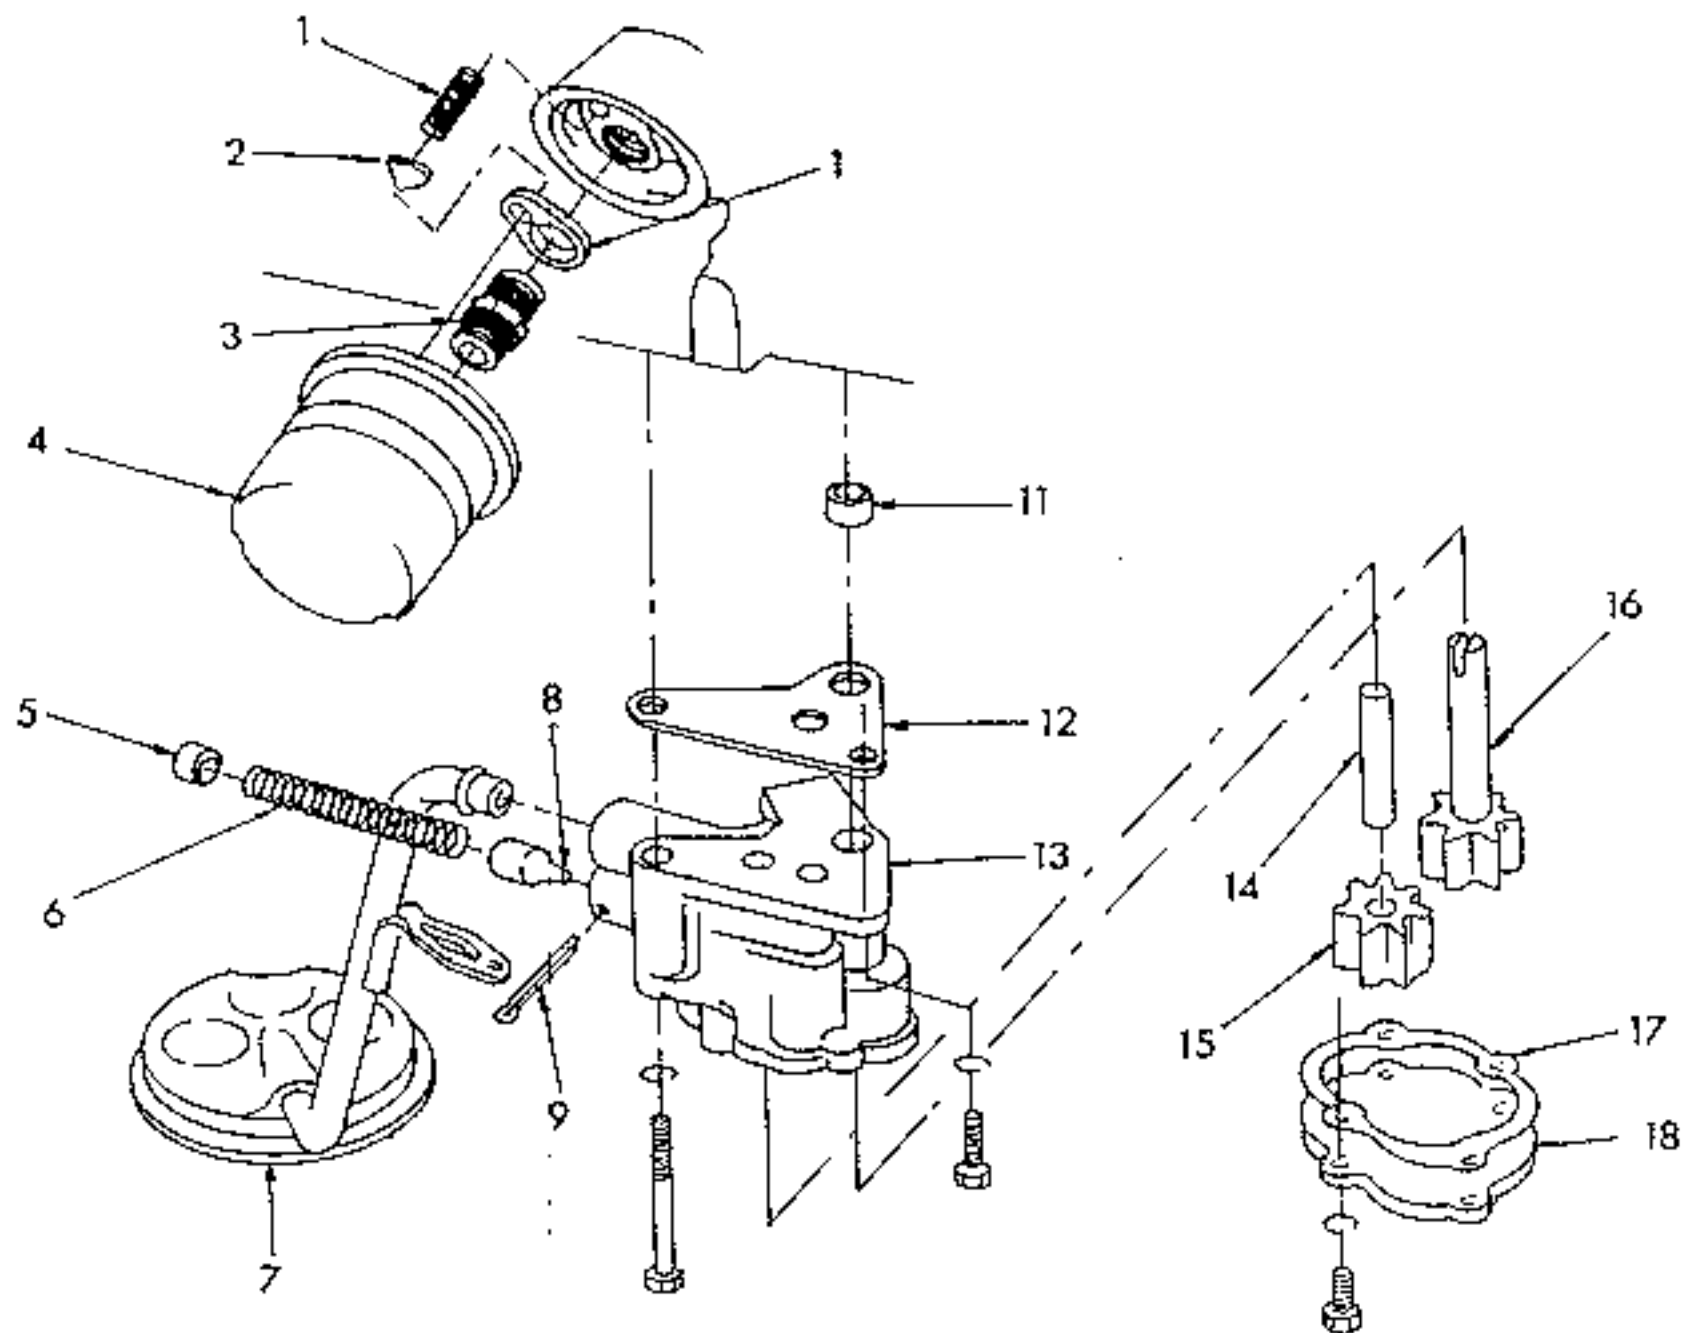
Montagebild der Ölpumpe des Sechszylindermotors.
